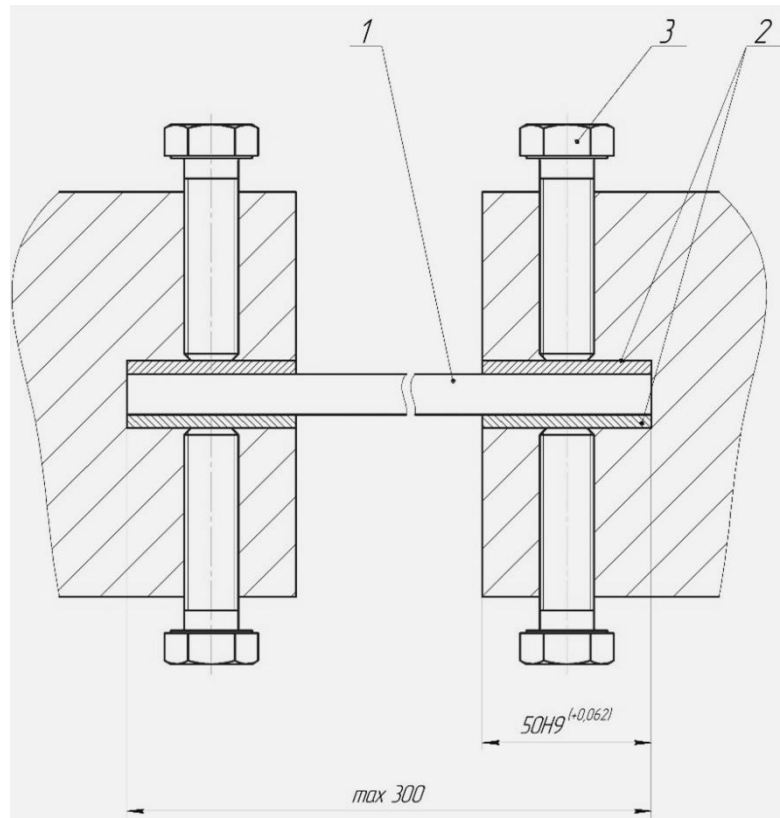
Схема установки и закрепления образца в захватах испытательной машины: 1 – образец, 2 – пластины, 3 – болты
